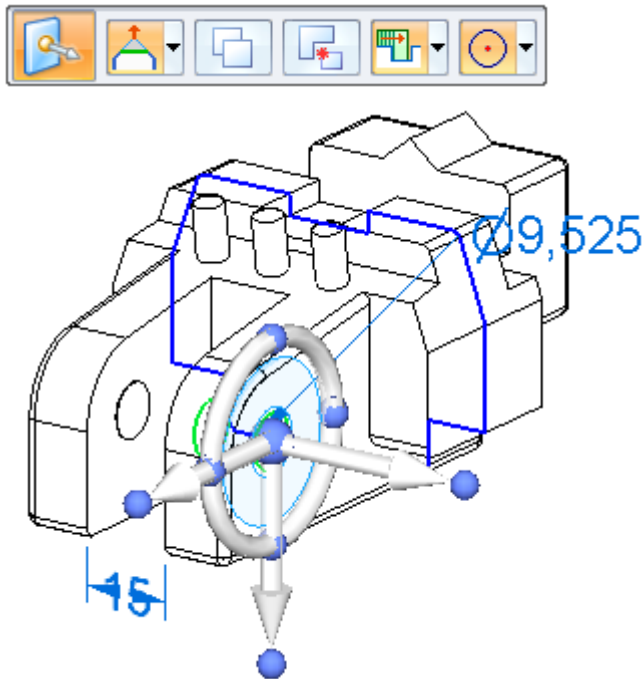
Das 3D-Steuerrad an der Bohrung
